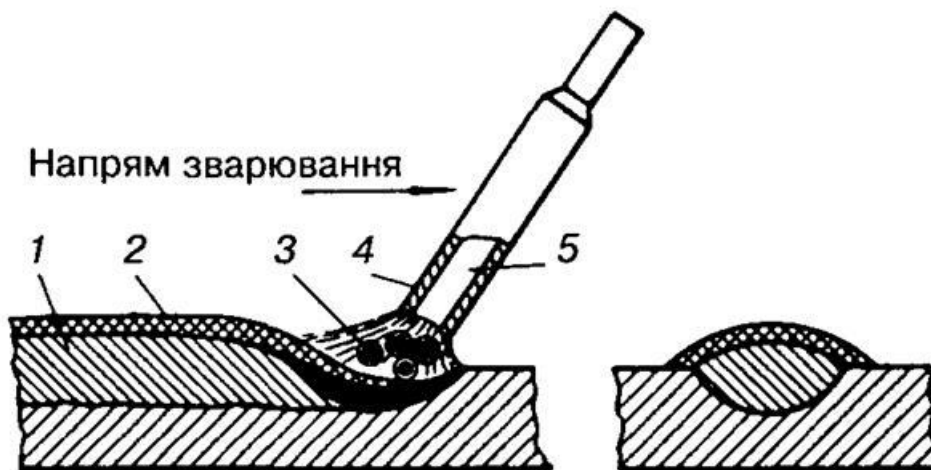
Схема зварювання електродом з покриттям: 1 – метал шва; 2 – шлакова кірка; 3 – краплини електродного металу в дузі; 4 – покриття; 5 - дріт
